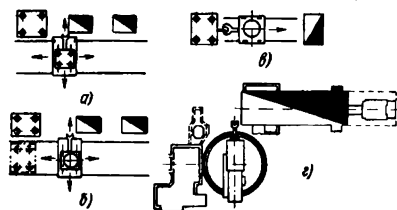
Схема расположения напольных рельсовых манипуляторов в агрегатах ковочных пресов: а — I типа; б — II типа; в — III и IV типа; г — V типа
